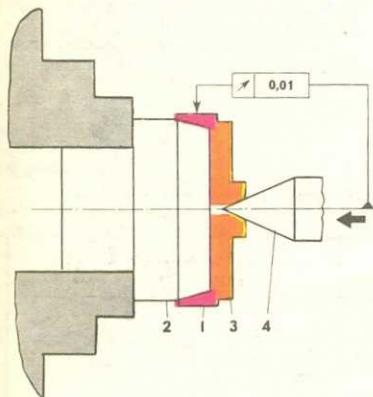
Установка наружного кольца подшипника на токарном станке для протачивания наружной поверхности: 1 — кольцо; 2 — оправка; 3 — шайба; 4 — вращающийся центр.
